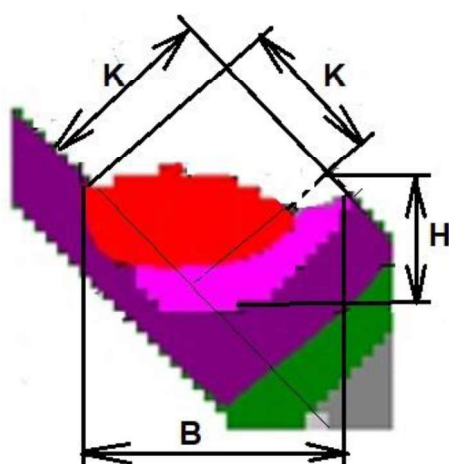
Профиль результирующего сварного шва (схематично):
